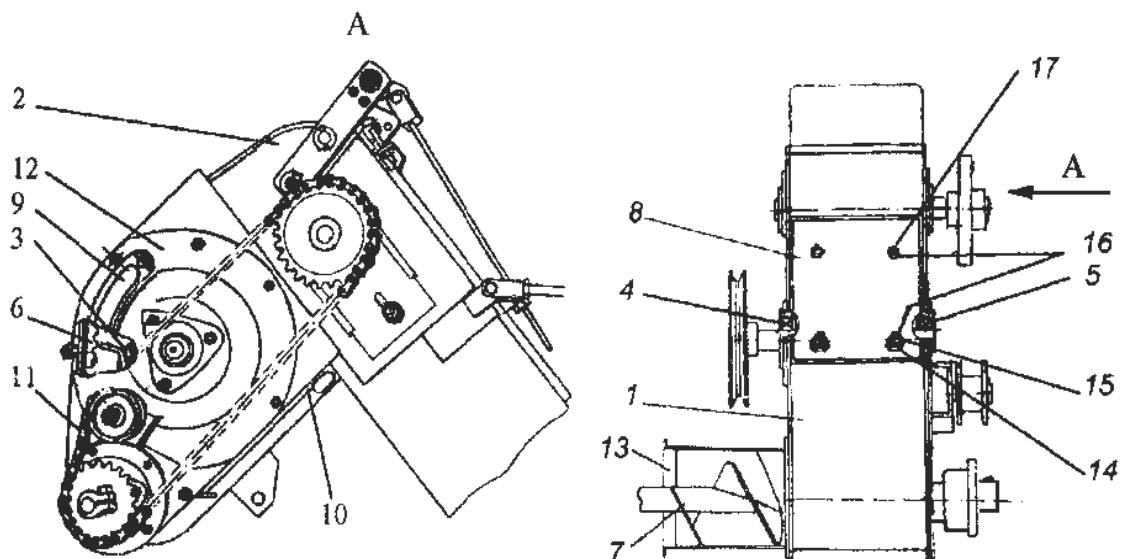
Домолачивающее устройство: 1 – корпус домолачивающего устройства; 2 – элеватор колосовой; 3 – барабан; 4, 5 – подшипники; 6 – дека; 7 – шнек; 8, 9, 10 – крышки; 11 – цепь; 12 – домолачивающее устройство; 13 – фланец; 14 – втулка; 15, 17 – болты; 16 – гайка
